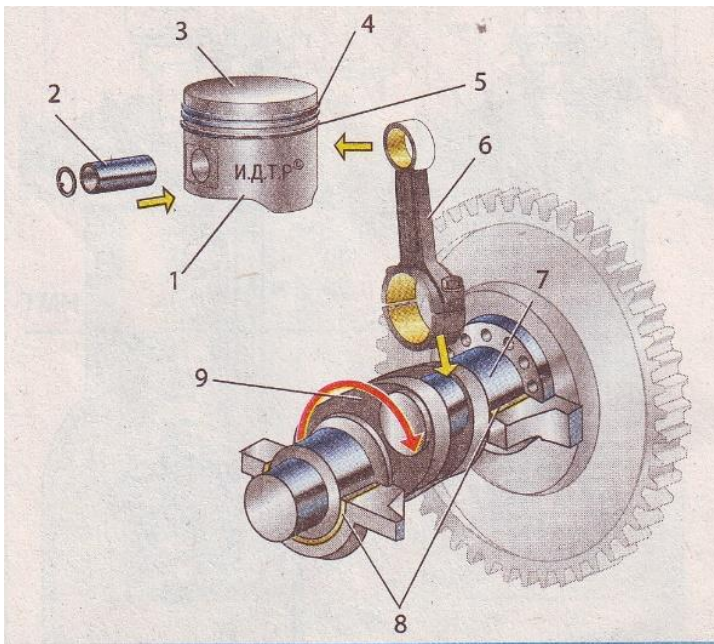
Поршень и коленчатый вал [5]: 1 – юбка поршня; 2 – палец и его стопорное кольцо; 3 – головка поршня; 4 компрессионные кольца; 5 – маслосъёмное кольцо; 6 – шатун; 7 – коленчатый вал; 8 – подшипники скольжения; 9 – кривошип коленчатого вала
